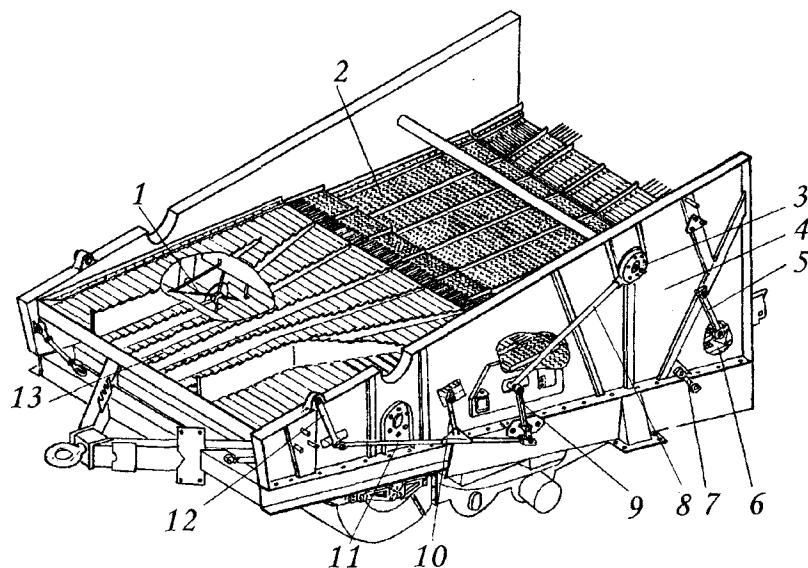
Общий вид механизма очистки КЗР-10: 1 – вентилятор; 2 – верхний решетный стан; 3 – маховик привода; 4 – несущая конструкция (рама); 5 – подвеска верхнего решетного стана; 6 – нижний решетный стан; 7 – подвеска нижнего решетного стана; 8 – шатун; 9 – двуплечий рычаг; 10 – стяжка; 11 – штанга; 12 – подвеска стрясной доски; 13 – стрясная доска.
